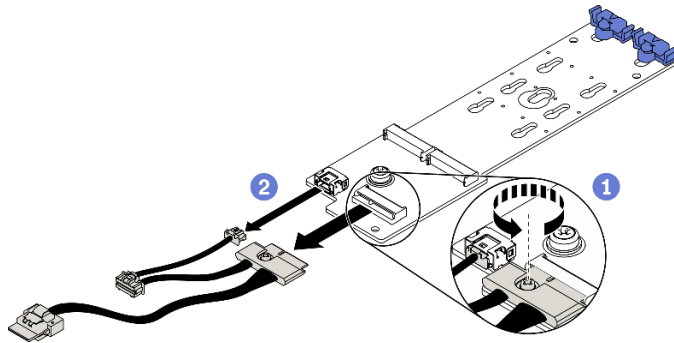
Entfernen der M.2-Kabel von der M.2-Rückwandplatine
